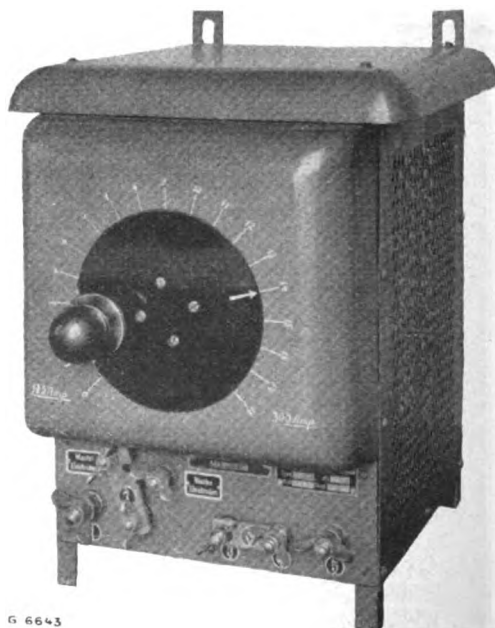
Induktiver Schweißstromregler in geschlossener Ausführung für eine Vielstellenschweißanlage für einen Schweißstrom von 50 bis 300 A.
